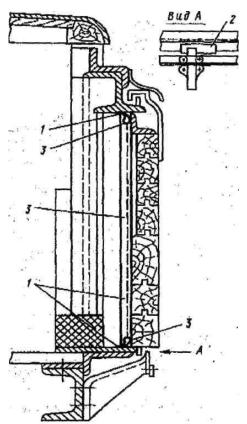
заделка щелей в рабочей двери вагона бумагой: 1 - место приклеивания; 2 - деревянный клин; 3 - валик из бумаги
